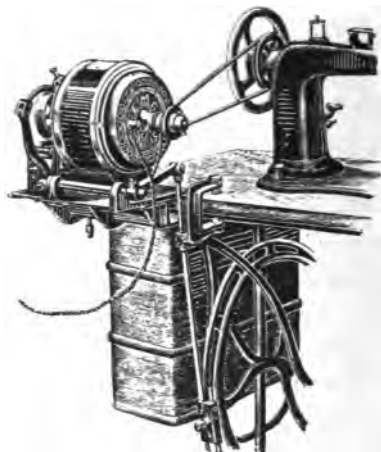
Disposition employée par la C^{ie} Emerson Electric pour la commande des machines à coudre.
